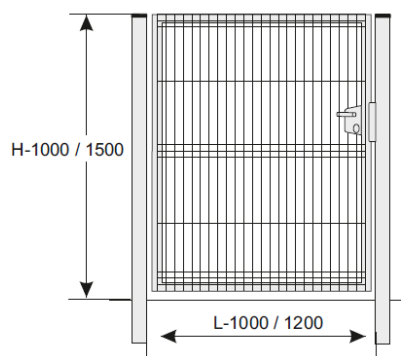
Konstrukcja panelu ogrodzeniowego
